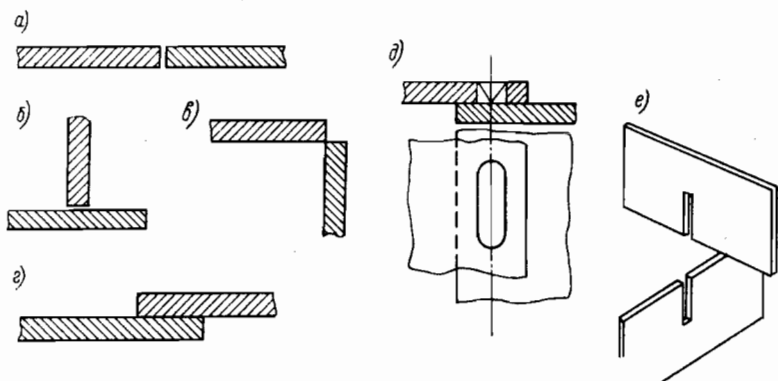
Типы сварных соединений: а — встык; б — тавровое; в — угловое; г — внакром; д — прорезное; е — гребенчатое
